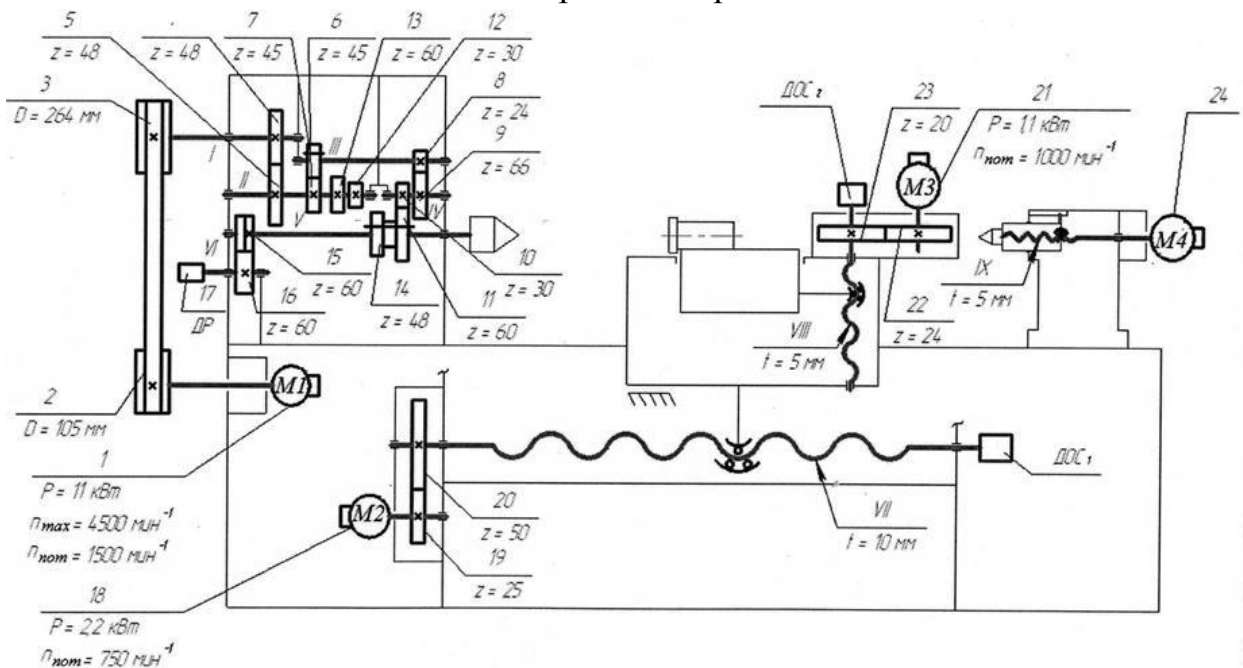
Кинематическая схема привода главного движения токарного станка с ЧПУ – переключение скорости блоками колес
